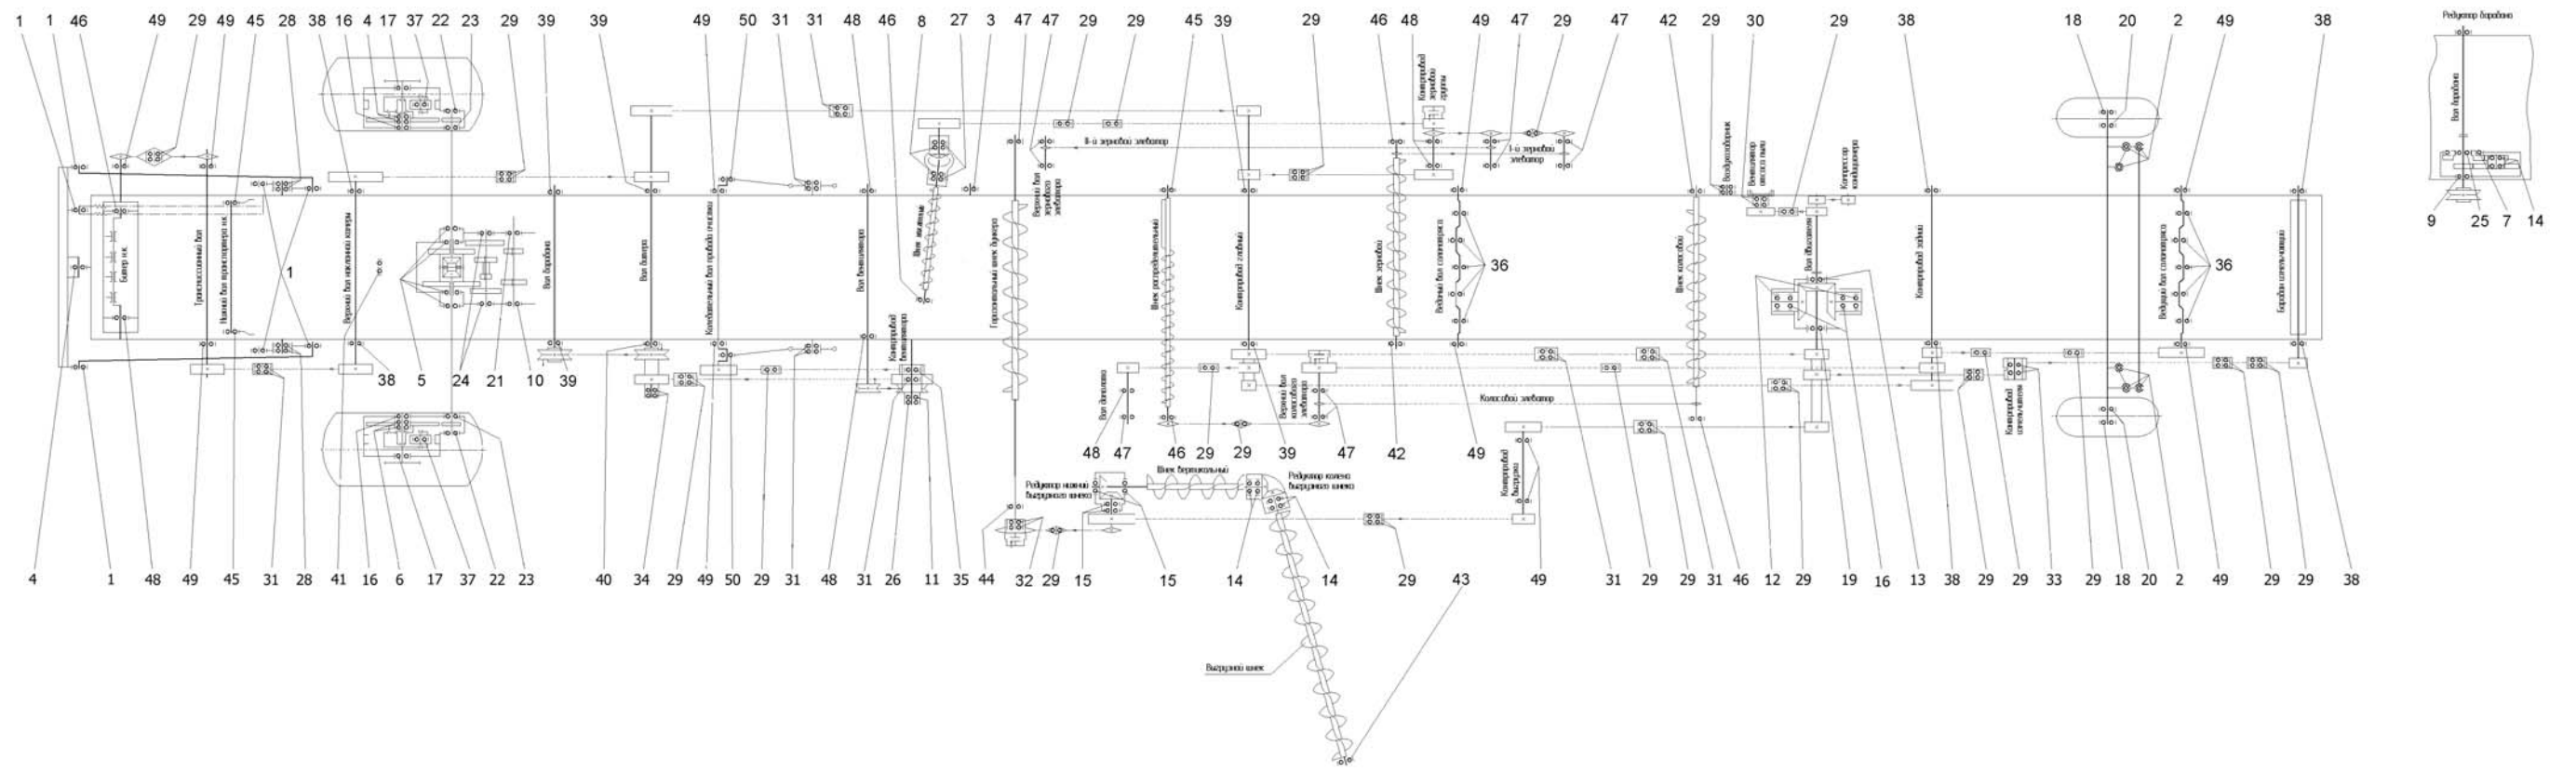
Схема расположения подшипников комбайна «ACROS-530»
